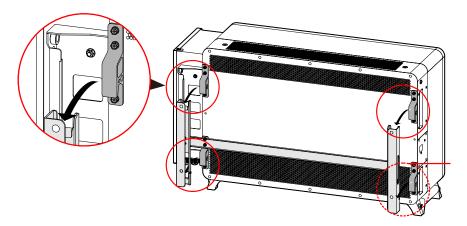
Montaggio dell'inverter sul supporto di installazione
